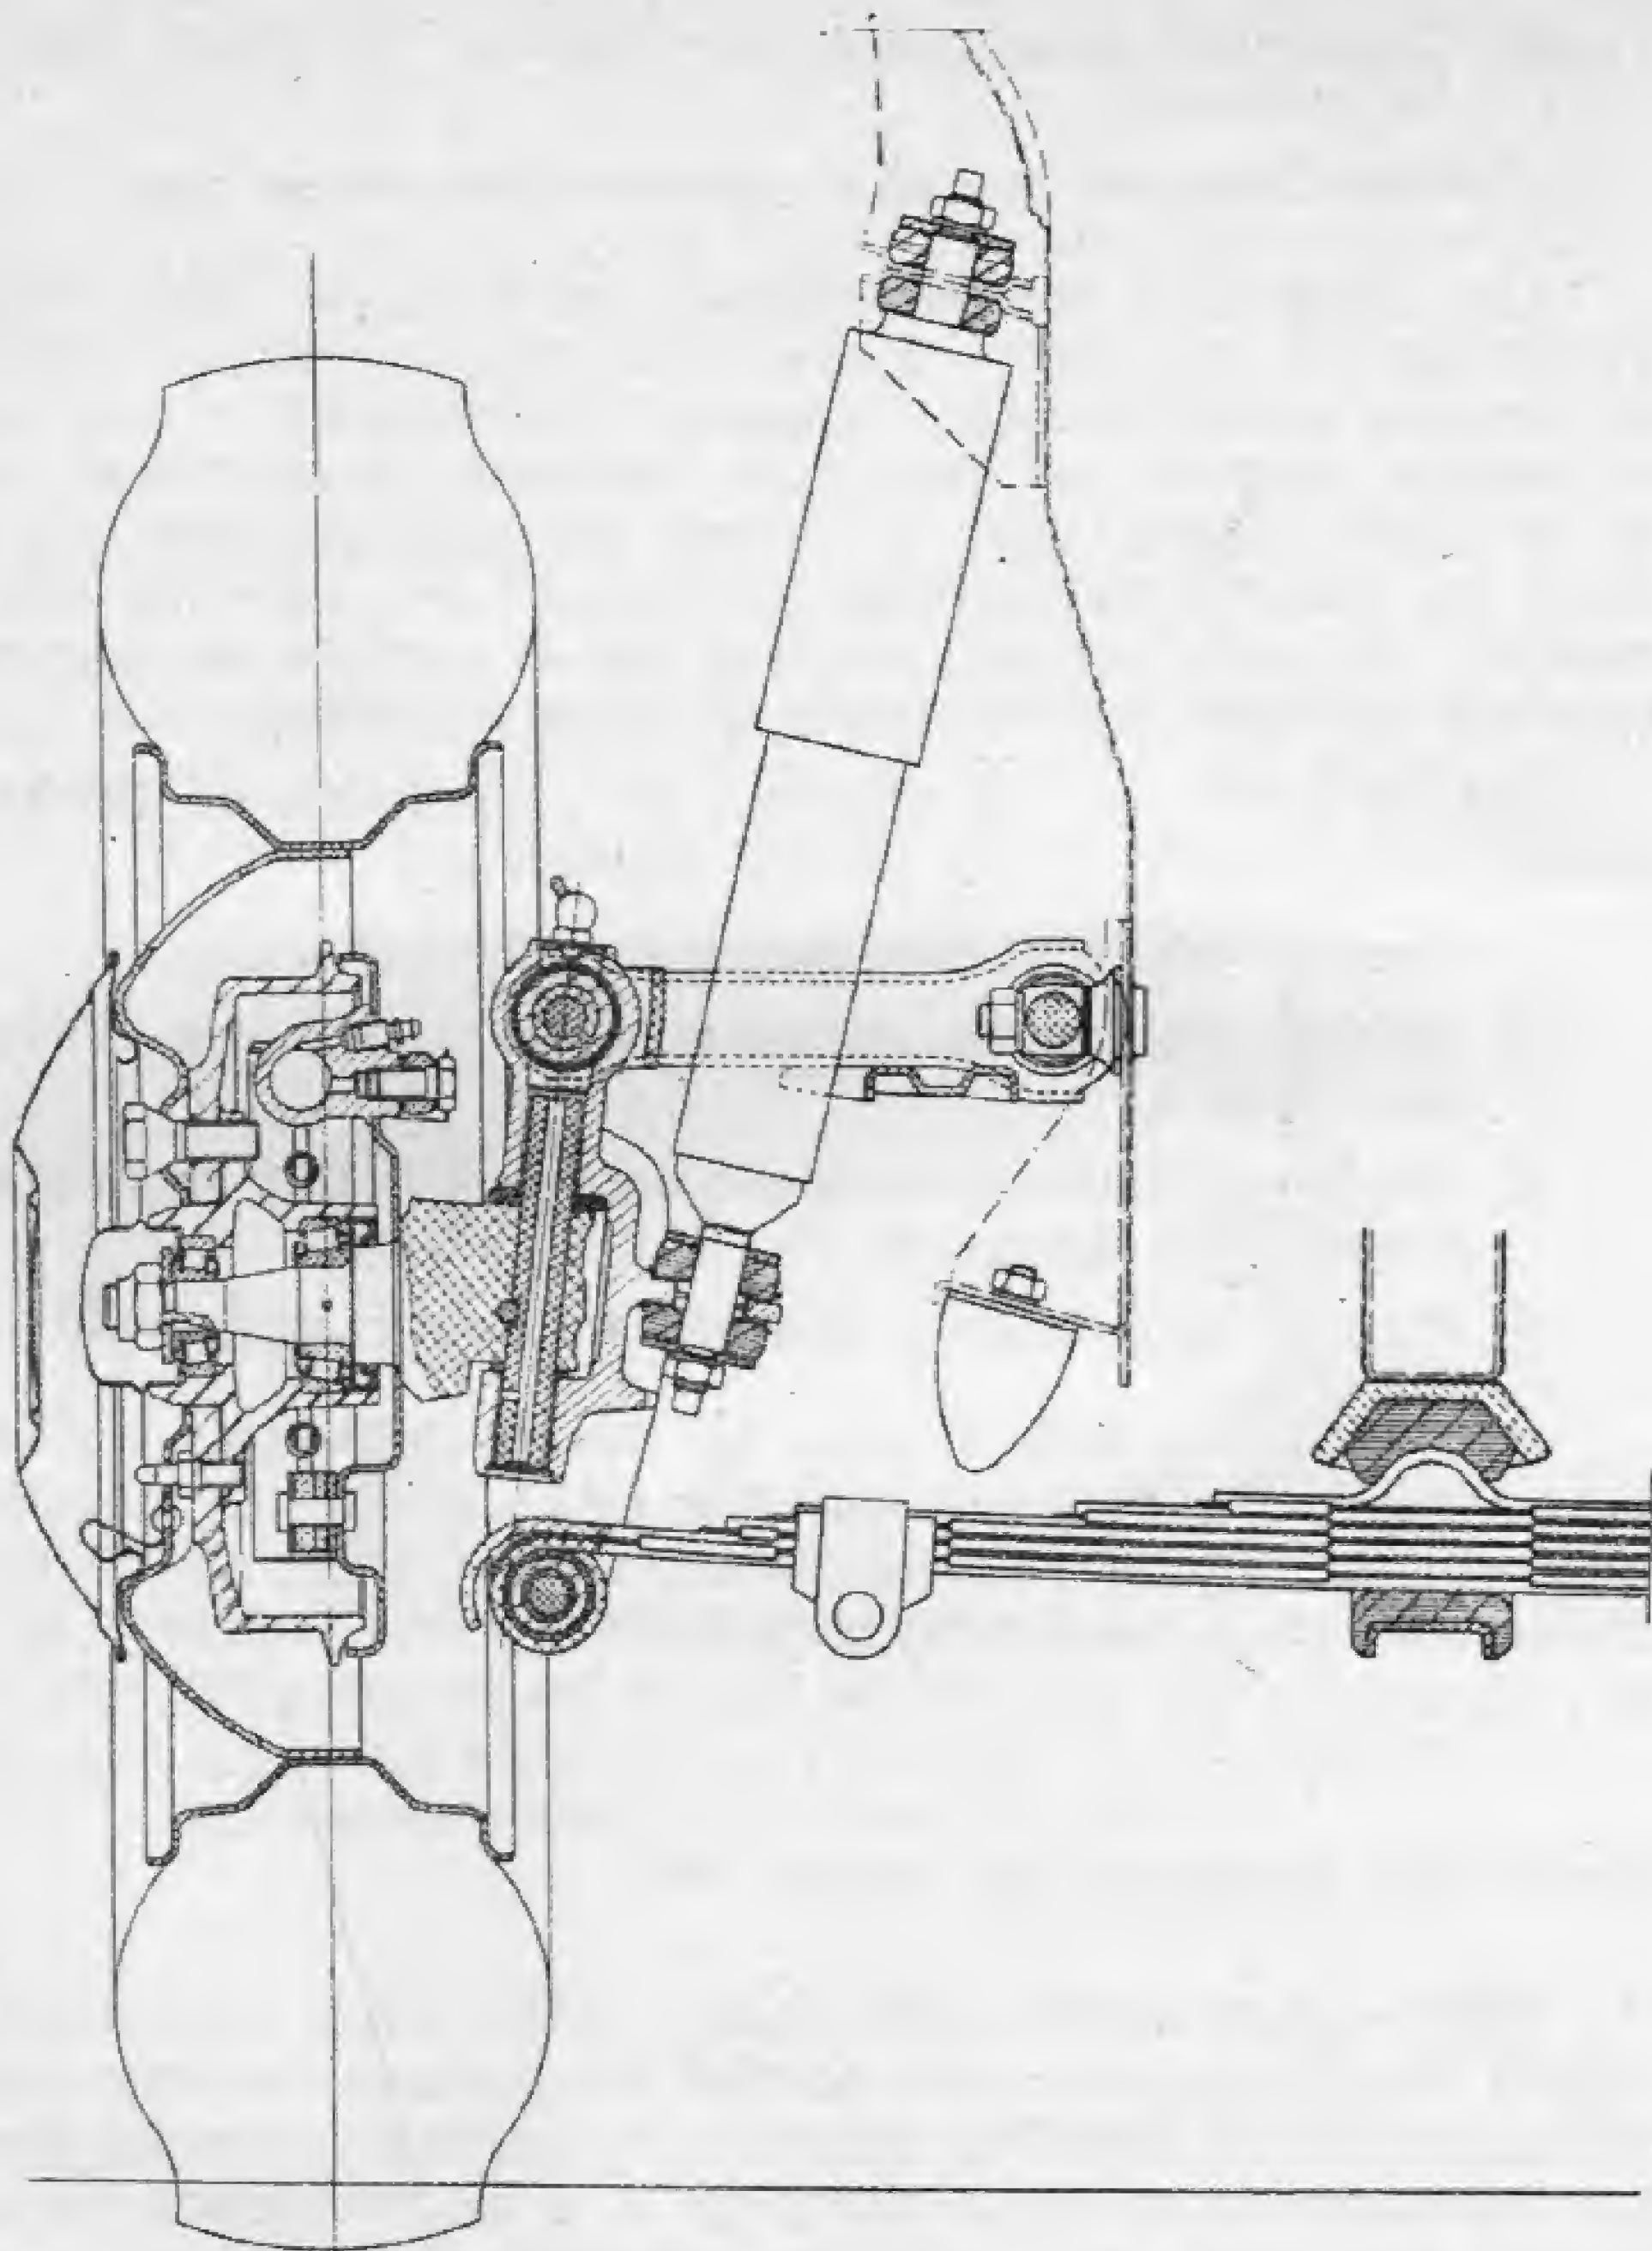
Vista en sección del conjunto suspensión y rueda delantera izquierda de los modelos 600 E-770 Coupé y 800 Coupé/Spider.
